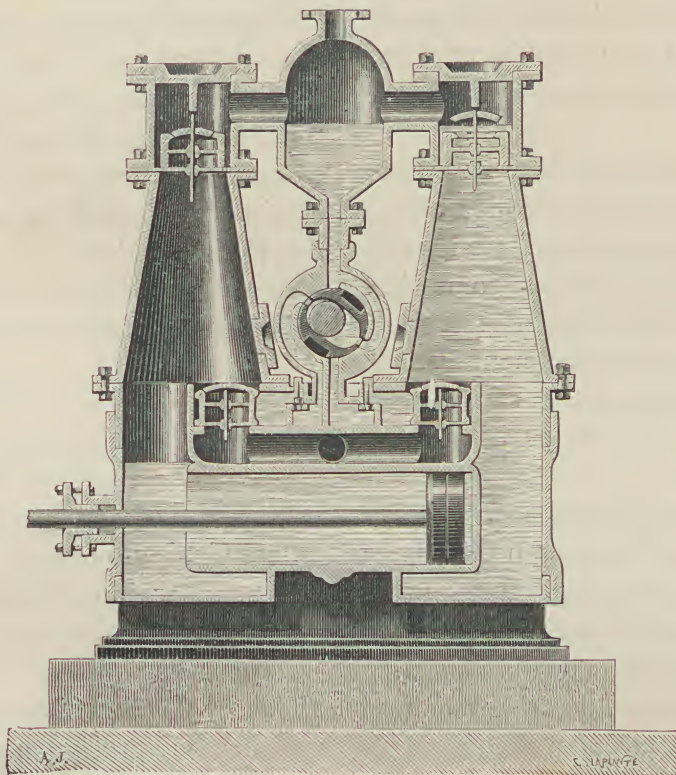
Compresor de doble efecto, sistema Fryer de Nueva York
